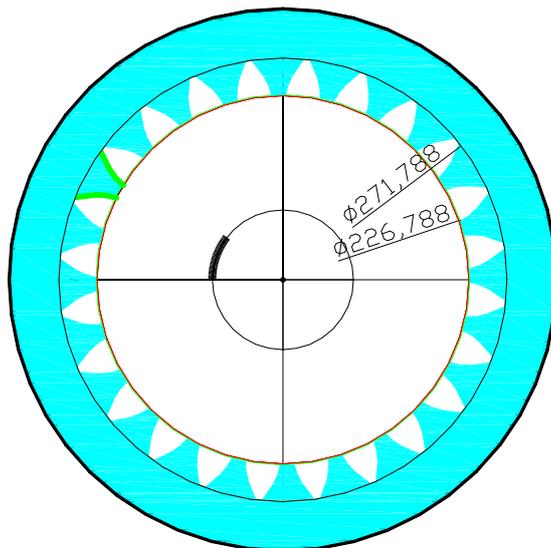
Модель зубчатого колеса с внутренними зубьями
